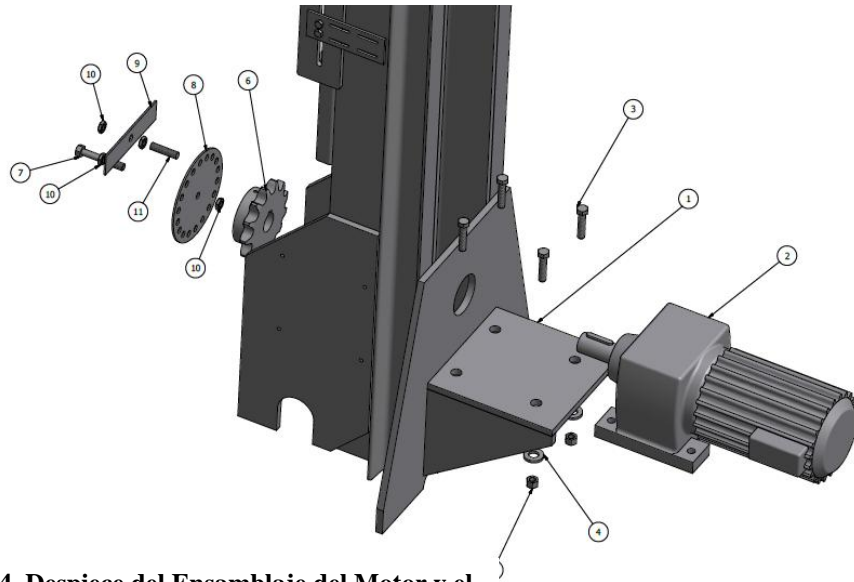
Despiece del Ensamblaje del Motor y el Sistema de Medición de Pulsos
